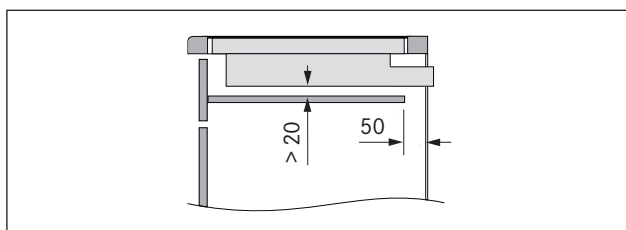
Vista laterale piano di protezione cavi e aerazione
